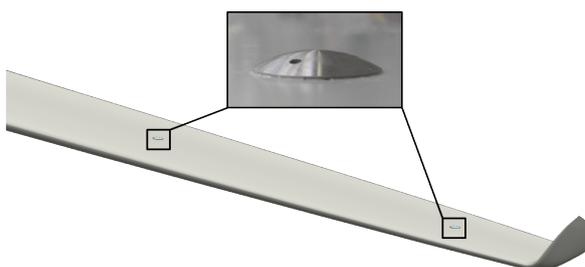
Rotorblatt mit Rezeptoren auf der Druck- und Saugseite, Beispiel
